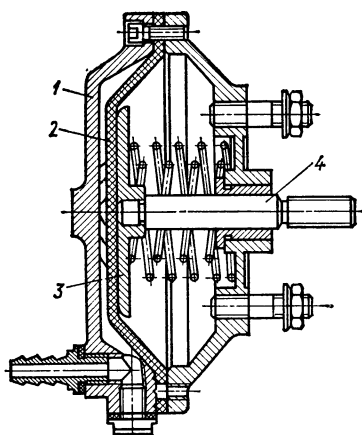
Одинарный пневмоцилиндр одностороннего действия с тарельчатой мембраной (1 — корпус; 2 — тарельчатая мембрана; 3 — опорная шайба; 4 — шток)
